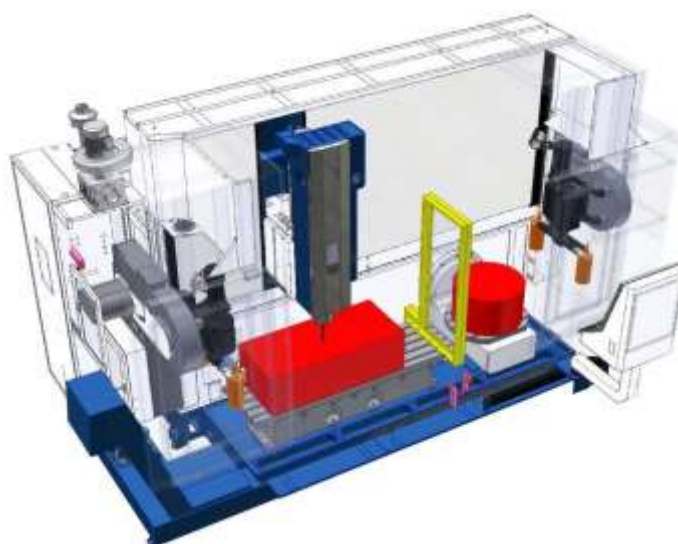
Разделение рабочей зоны станка SPINNER U2520
